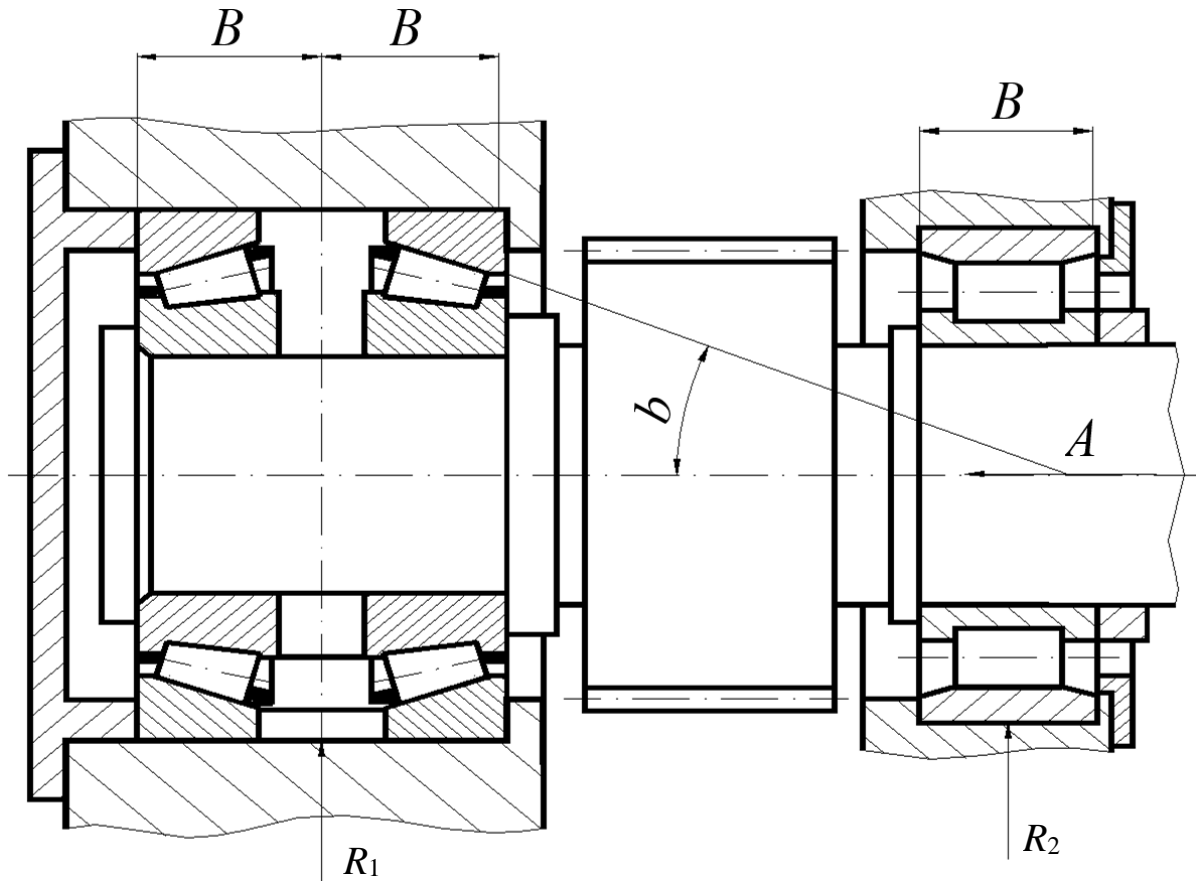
Конструкция части редуктора с коническими подшипниками
